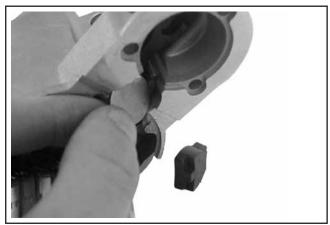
Drehzapfenhülse und Grundplatte entfernen.
